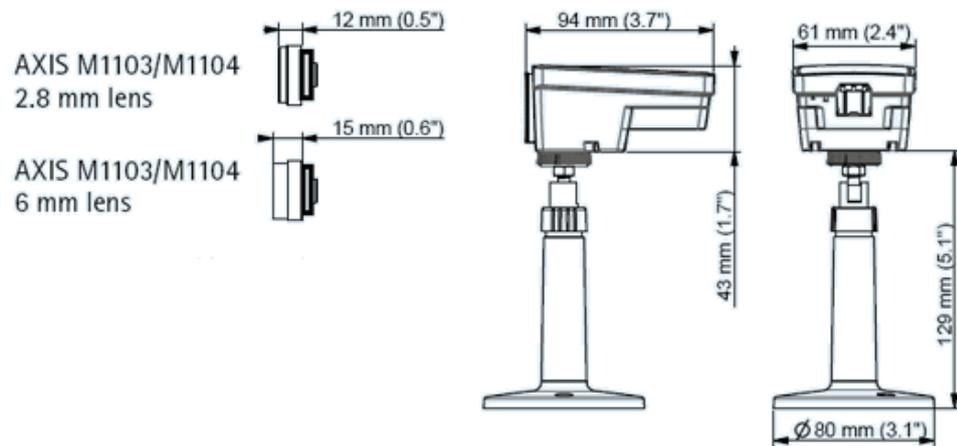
Dimensiones de Cámara IP Axis M1103[20]
